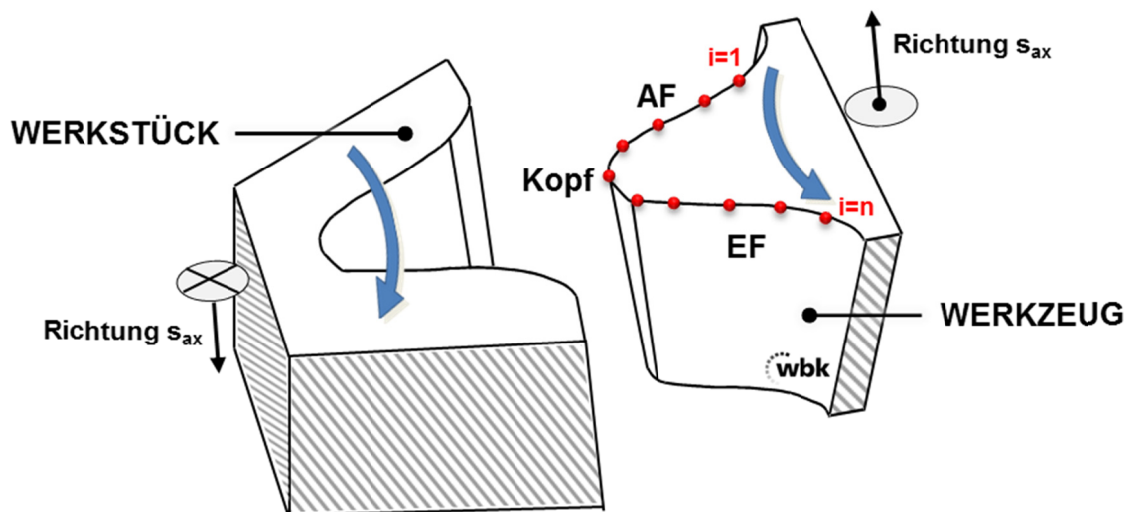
Bezeichnungen am Werkzeugzahn
